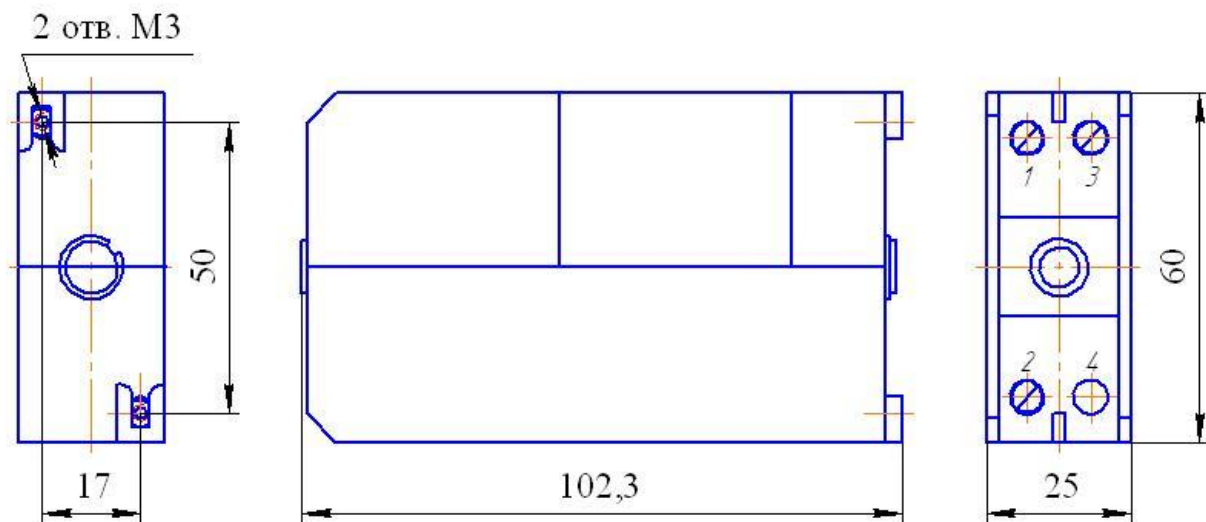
Габаритные и установочные размеры ОПН для KV2-630
